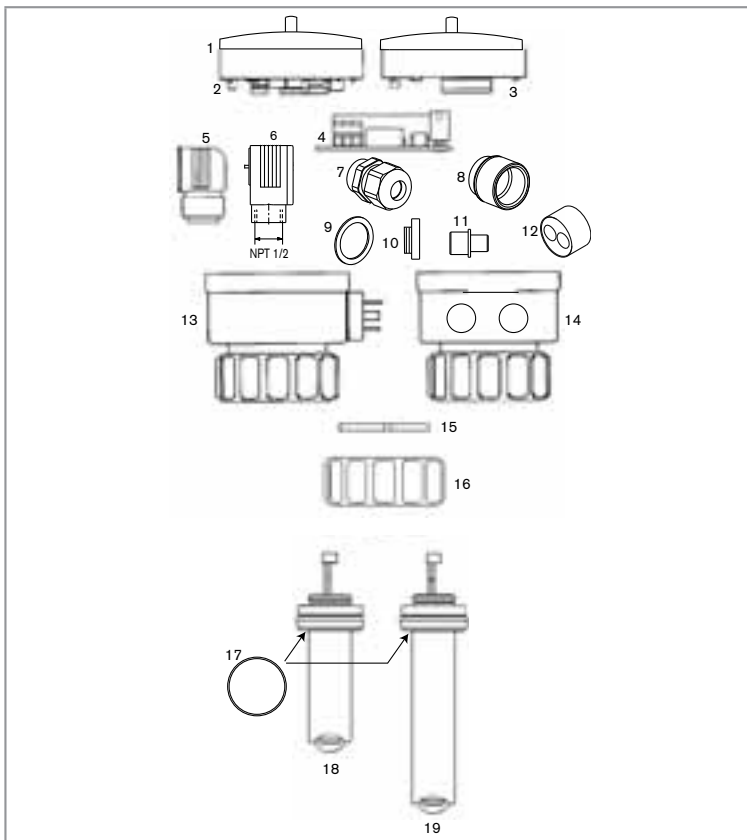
Vue éclatée des pièces de rechange 8025 version compacte
